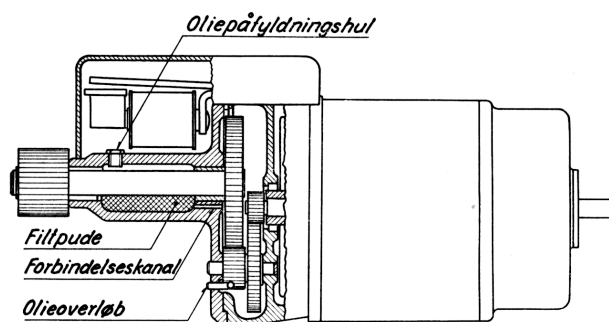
Motorgruppe for DSB 1957 drev (m. b.). Oliepåfyldning i gearkasse.
